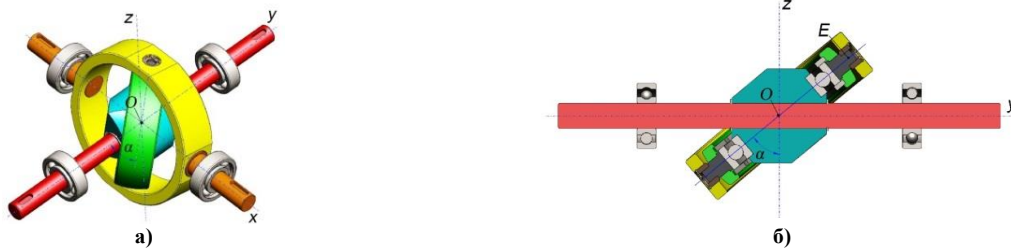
Розрахункова схема сферичного кривошипно-повзунного механізму
